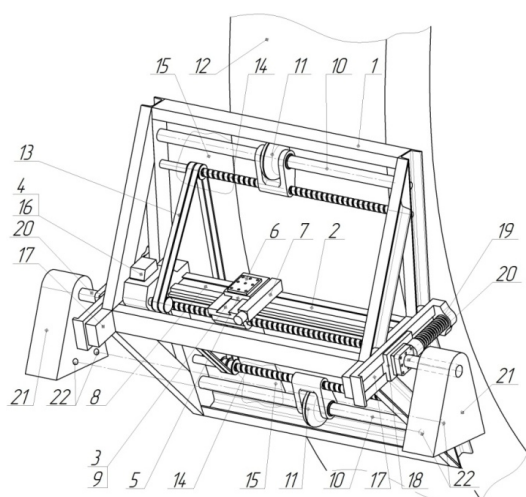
Схема станка для обработки поверхностей крупногабаритных деталей-тел вращения
